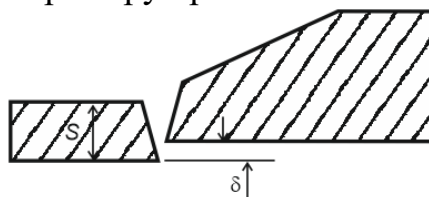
Наклонный шов при сварке труб различной толщины
